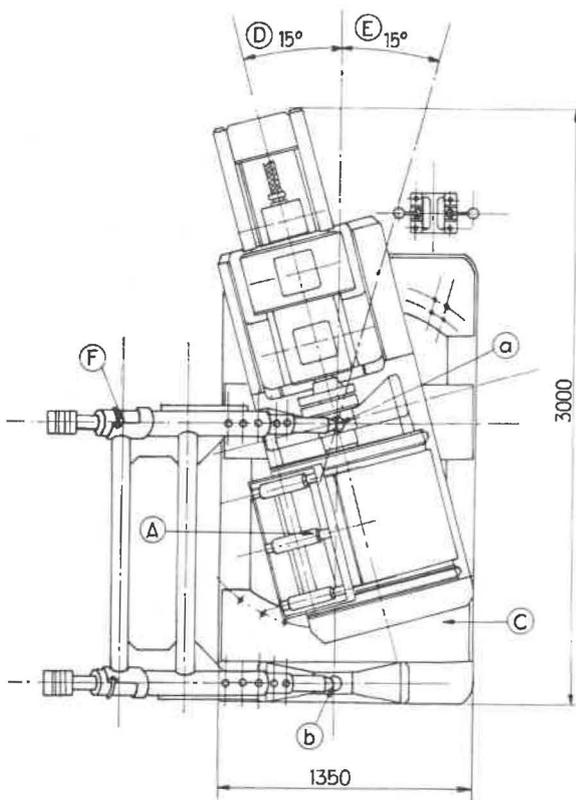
Treuil Escol type ESP/75. Vue en plan.
